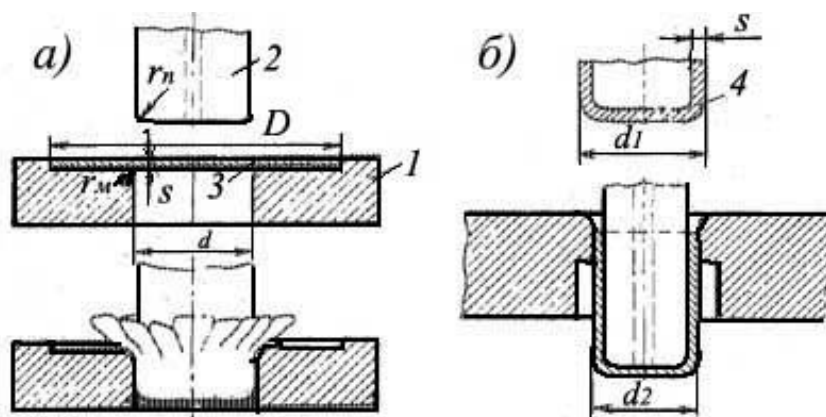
Схема процесса вытяжки: d_1 — диаметр полой заготовки после первой операции; d_2 — диаметр полой заготовки после второй операции
